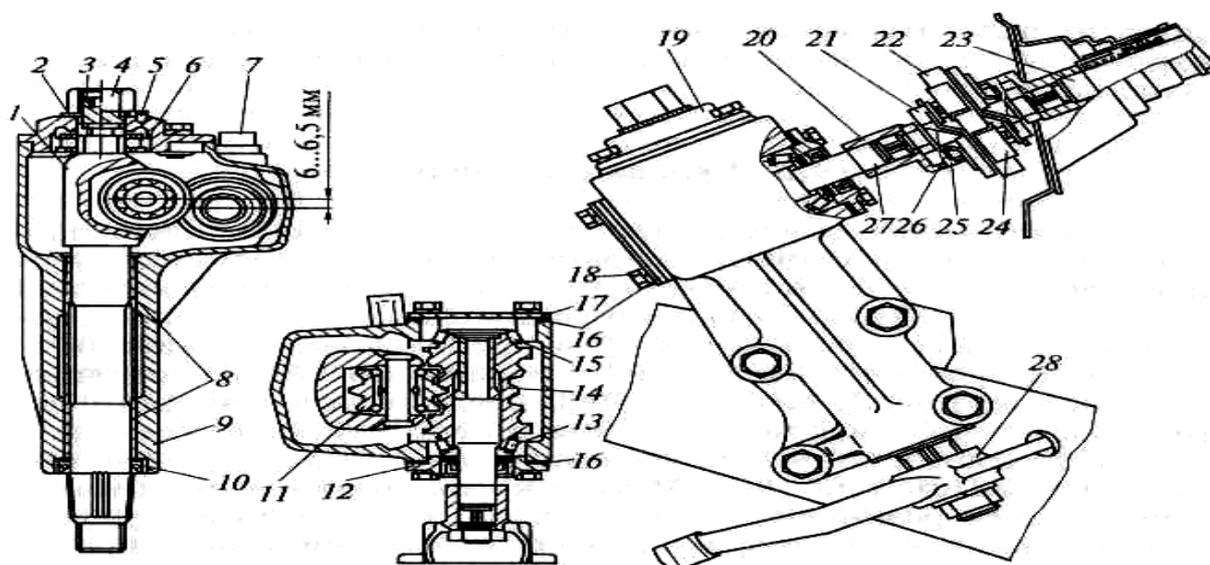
Рулевой механизм: 1 — вал сошки; 2 — стопорная шайба; 3 — регулировочный винт; 4 — колпачковая гайка; 5 — штифт; 6 — роликовый подшипник; 7 — втулки; 8 — втулки; 9 — картер; 10 — сальник; 11 — задняя крышка; 12 — задняя крышка; 13 и 15 — задний и передний подшипники червяка; 14 — червяк; 16 — регулировочные прокладки; 17 — передняя крышка; 18 — болт сливного отверстия; 19 — верхняя крышка; 20 — фланец; 21 — шпилька; 22 — эластичная соединительная муфта; 23 — верхний вал; 24 — усилительная пластина; 25 — гайка; 26 — стопорная пластина; 27 — нижний вал; 28 — сошка.
